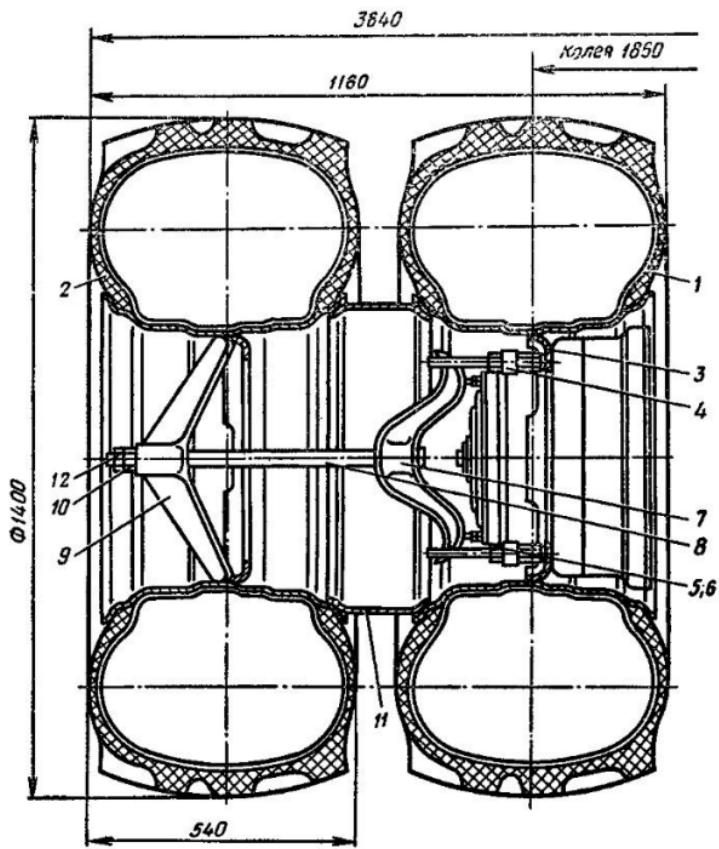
Приспособление для сдавливания колес трактора Т-150К:
